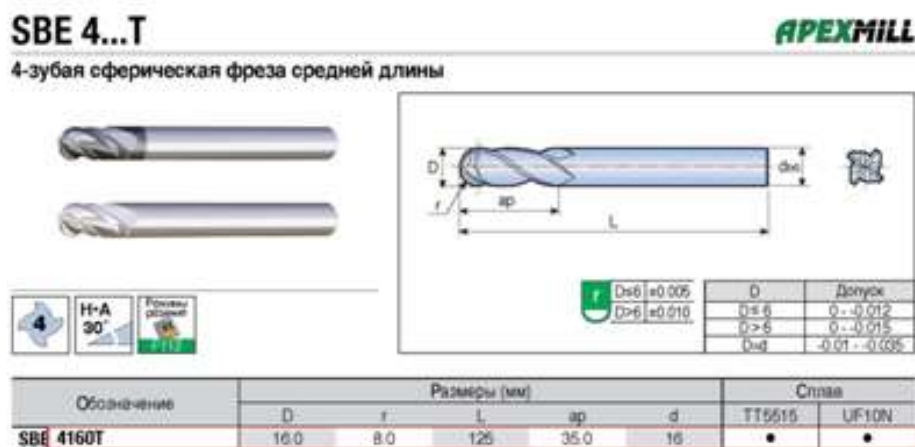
Геометрические параметры режущего инструмента обрабатываемый заготовки
